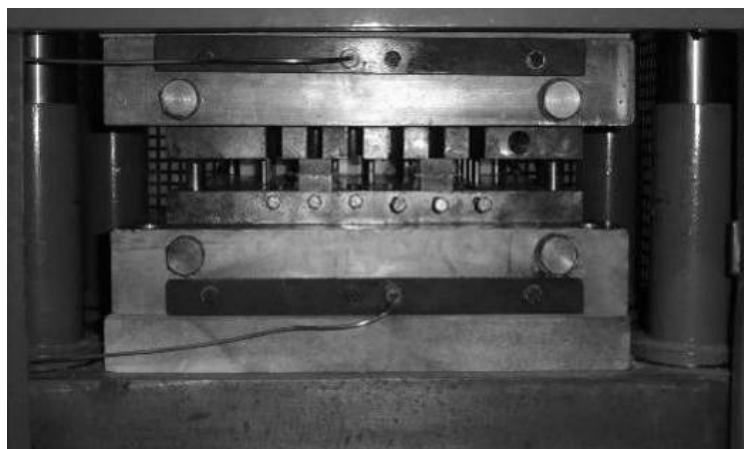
Molde com provetes DCB colocado na prensa.
